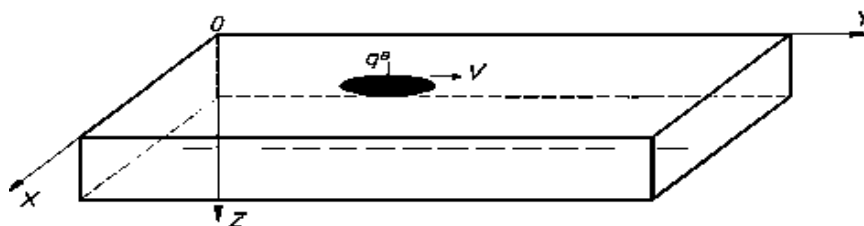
Розрахункова схема процесу лазерного формоутворення
